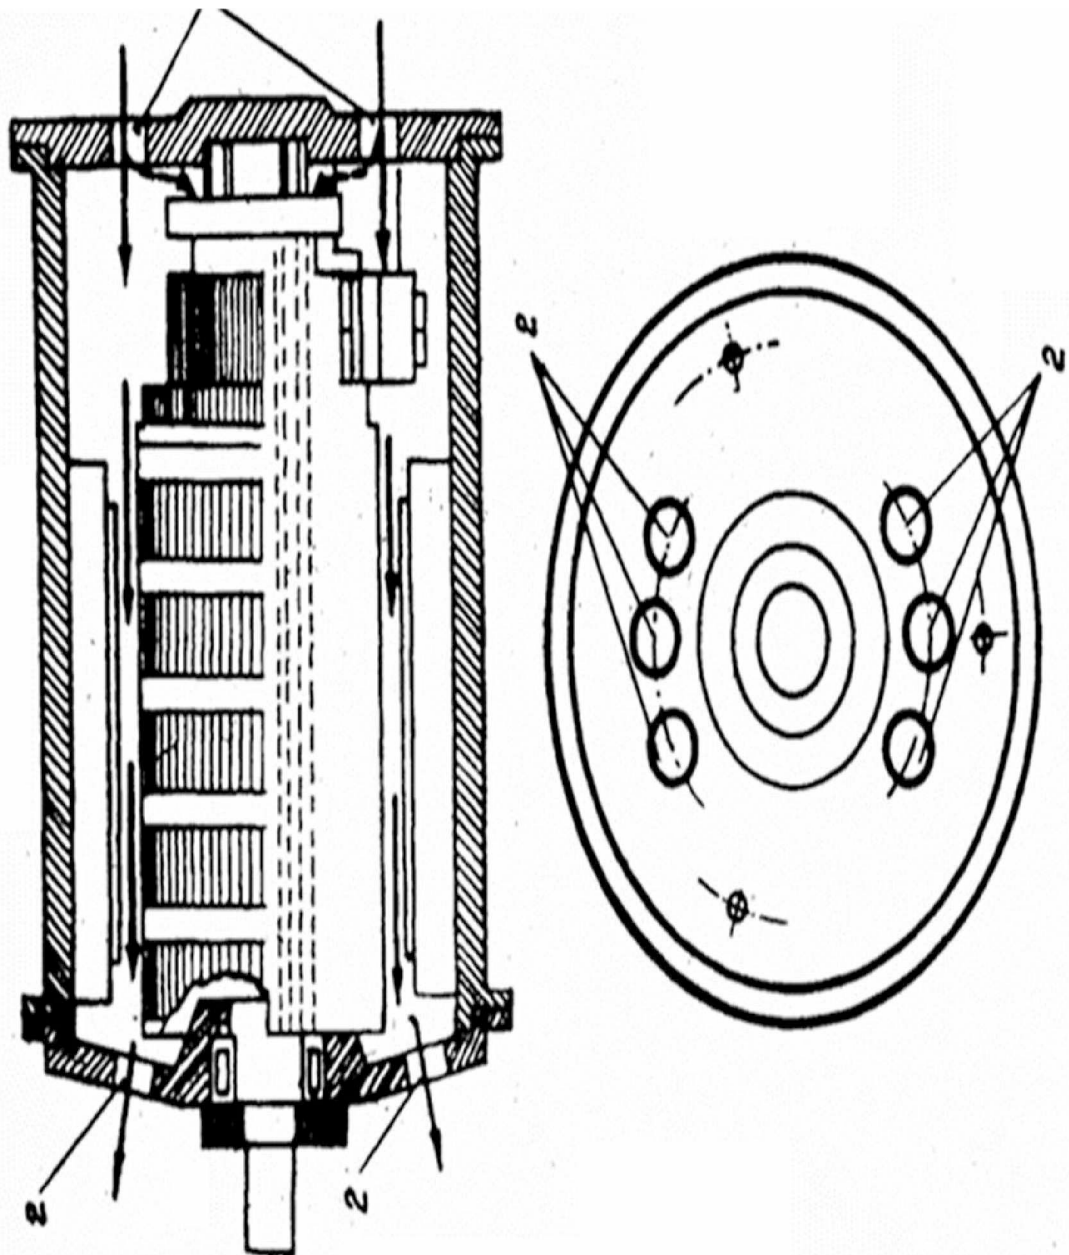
Схема вентиляції тягового двигуна ДК-809А: 1, 2 — вентиляційні отвори
